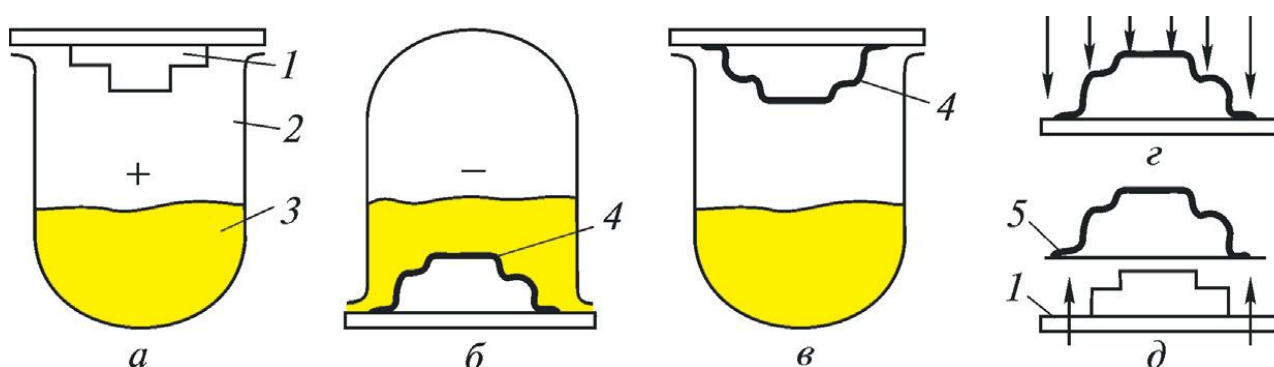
Схема бункерного способу виготовлення оболонкових форм:
